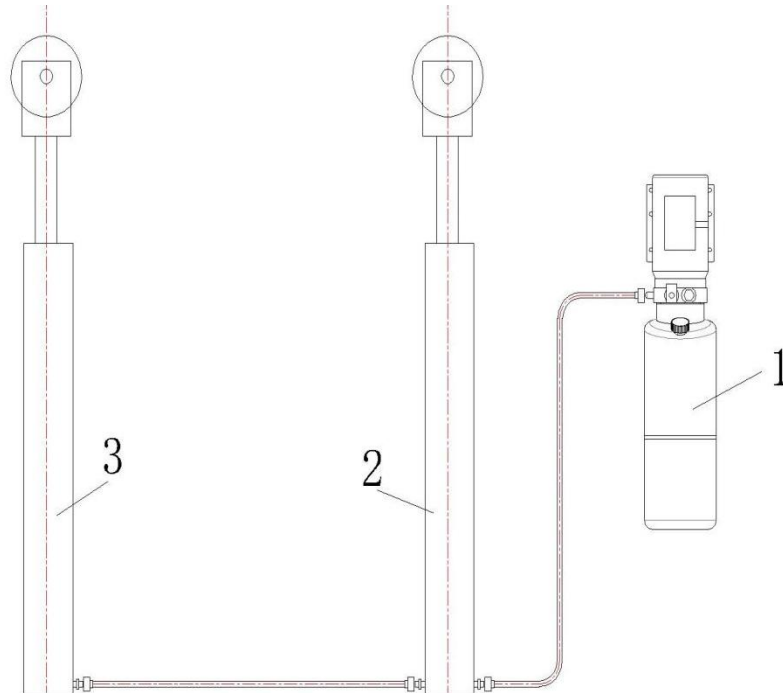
Anschlussplan des Hydrauliksystems der Hebebühne
